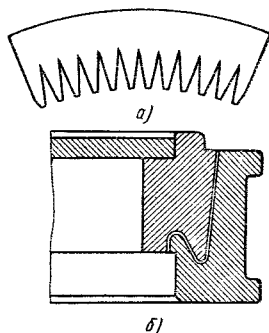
Заготовка (а) и пресс-форма (б) для манжеты
